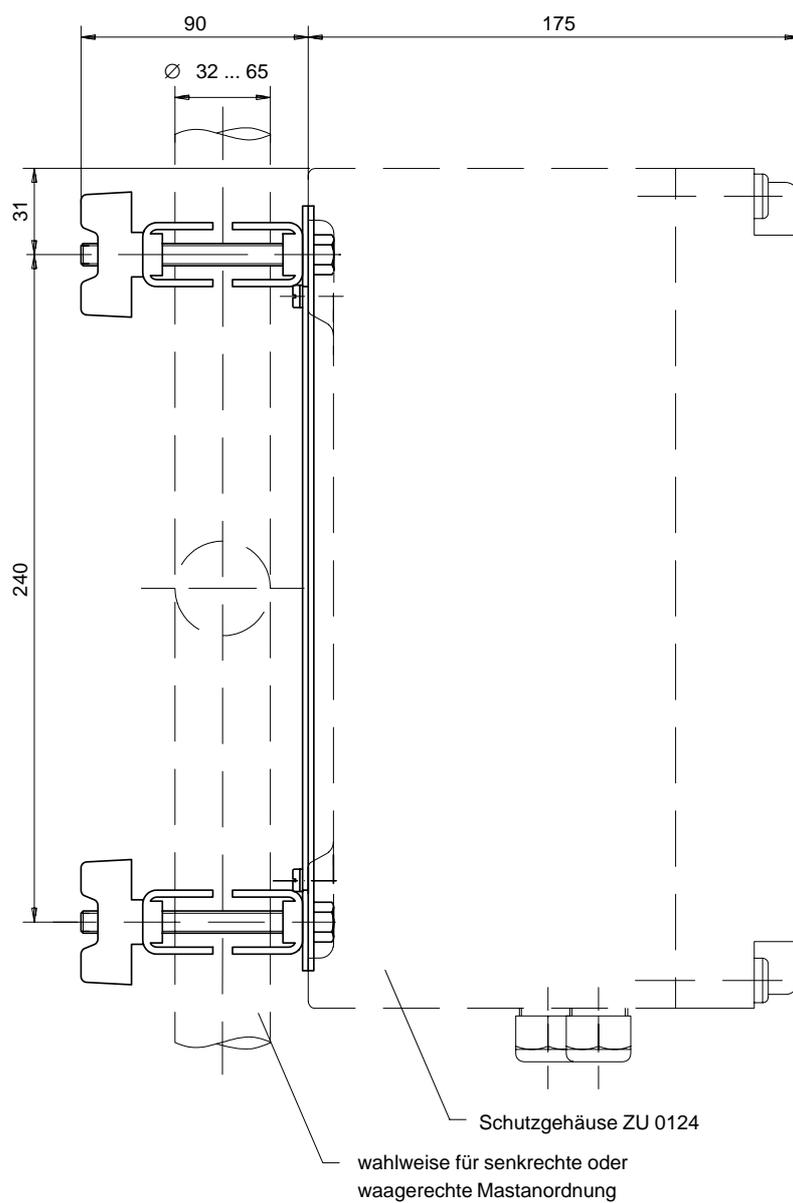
Mastschellen-Satz ZU 0128 für Schutzgehäuse ZU 0124
